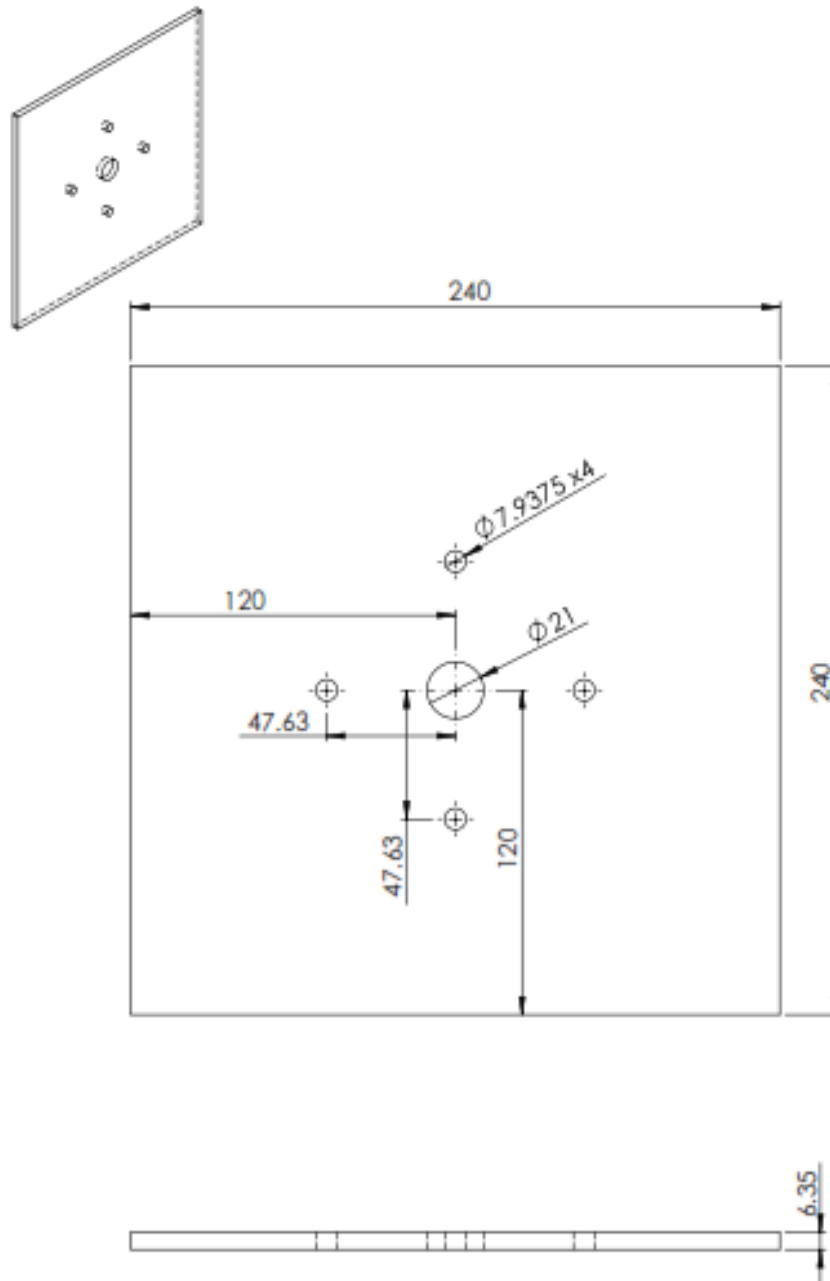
Plano de la lámina superior de la carcasa (cotas en mm). Fuente: Autores.
